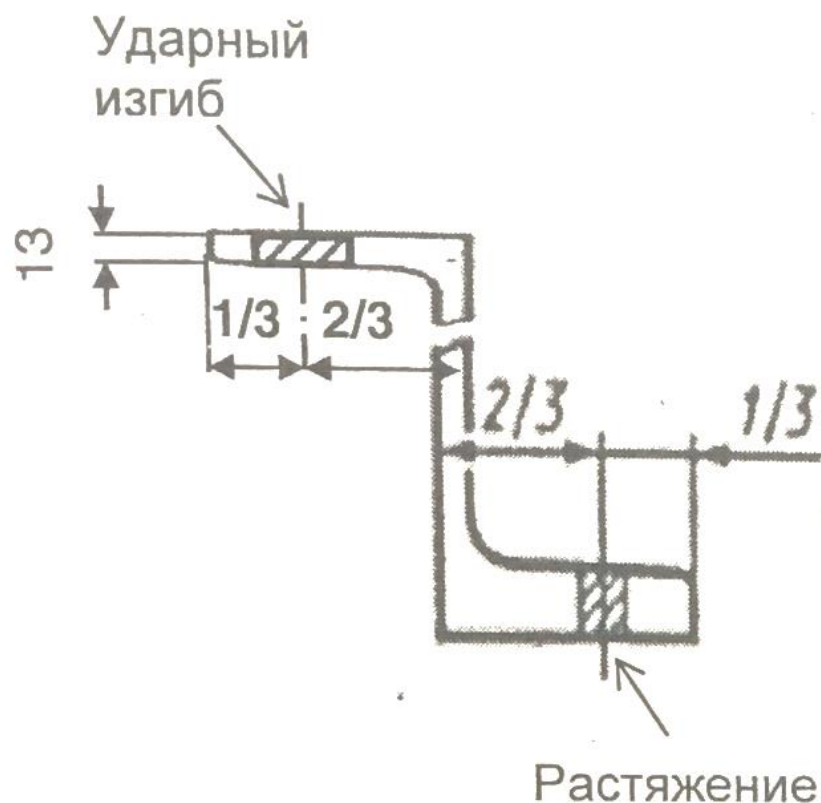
Схема отбора заготовок на испытания механических свойств
